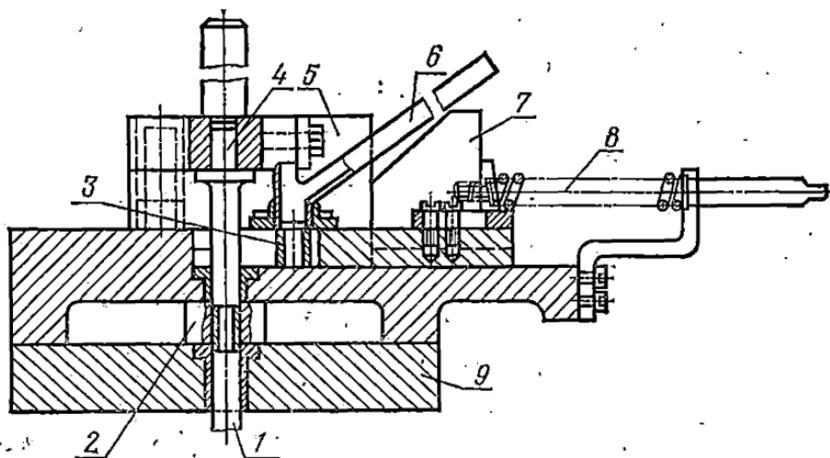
Полуавтоматическое приспособление к прессу для запрессовки втулок в верхнюю головку шатуна:
